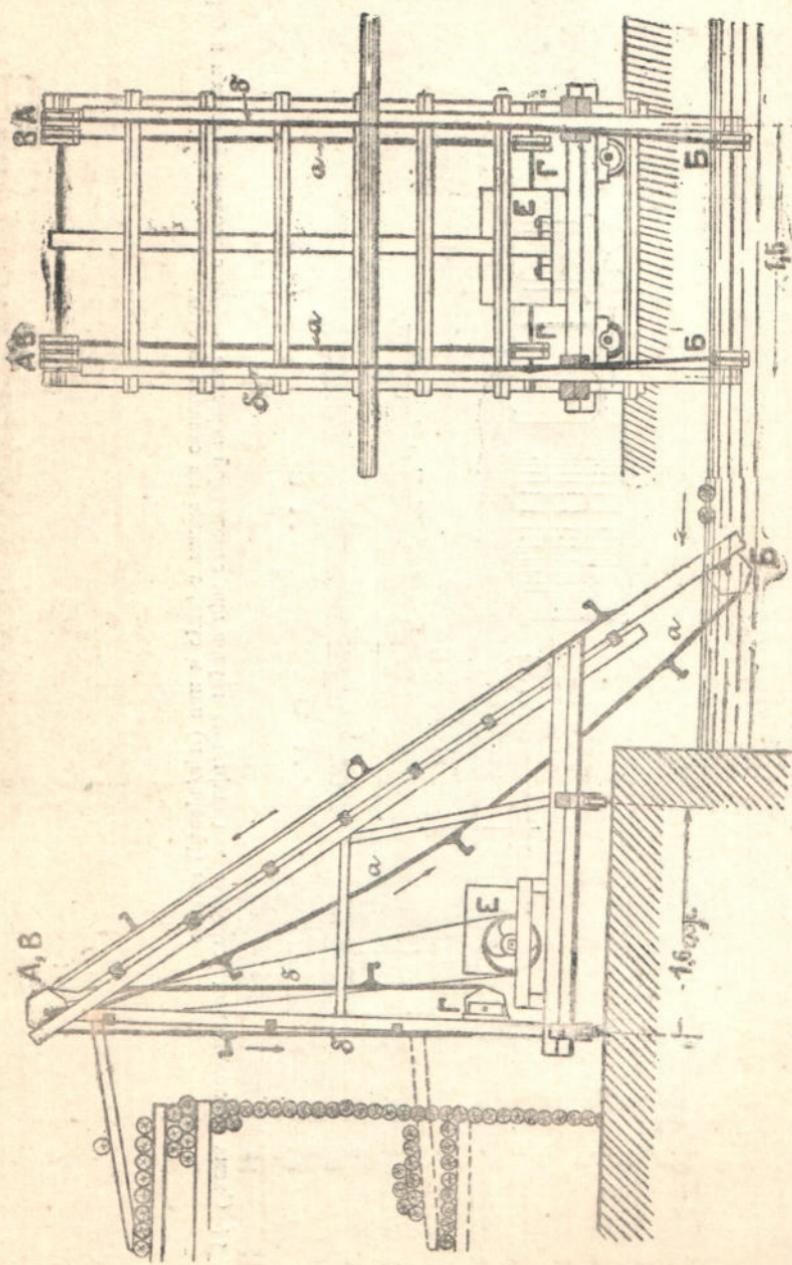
Устройство поперечной лесотаски для подъема бревен из воды на берег. (Слева—вид сбоку, справа—фасад с волы.)
